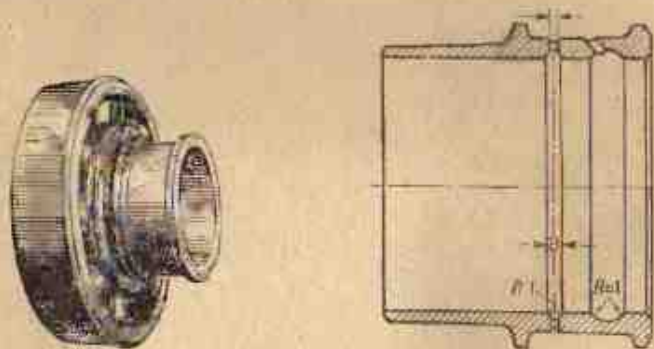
Общий вид распорной втулки с упорным подшипником и ее разрез
